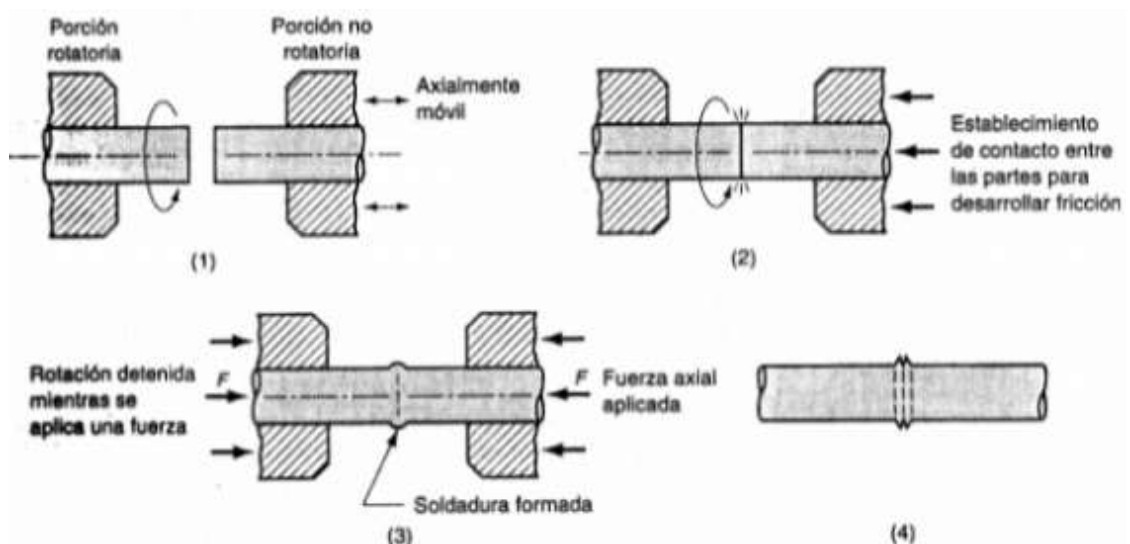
(1) Soldadura por fricción (FRW) parte rotatoria, sin contacto; (2) establecimiento de contacto entre las partes para generar calor por fricción; (3) rotación detenida y presión axial aplicada; y (4) soldadura terminada
